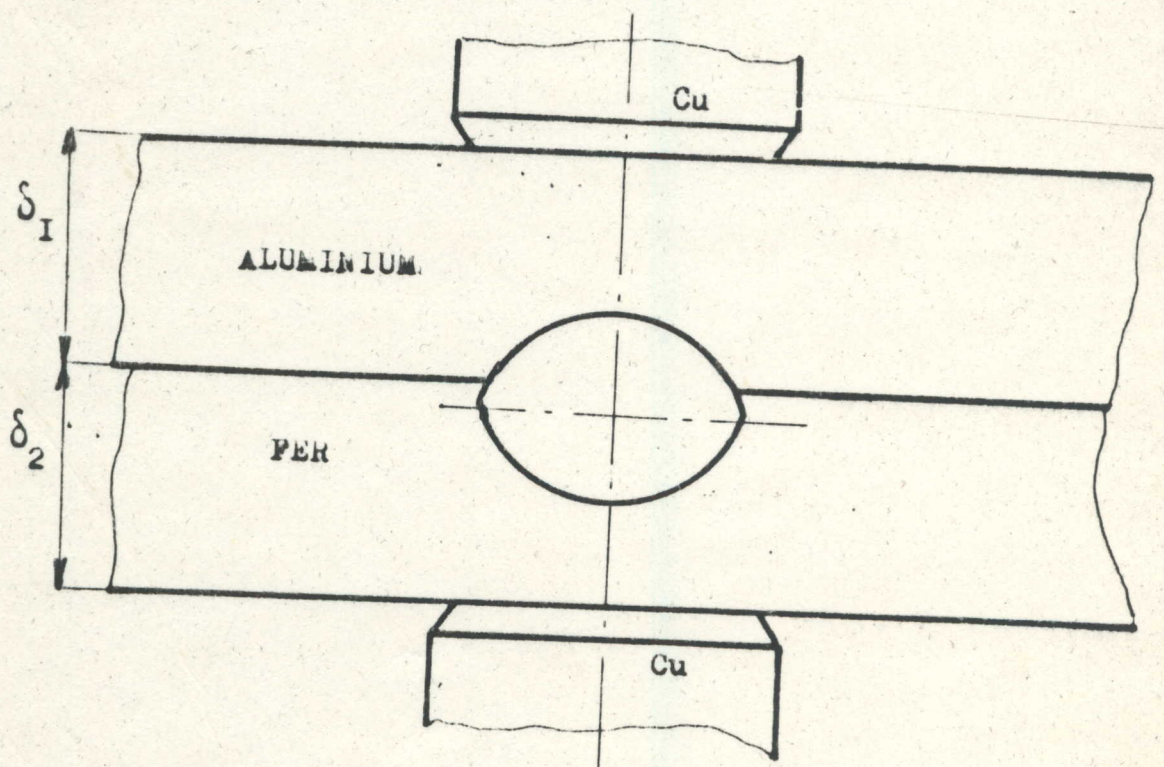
Soudage avec pièces de différentes matières .
